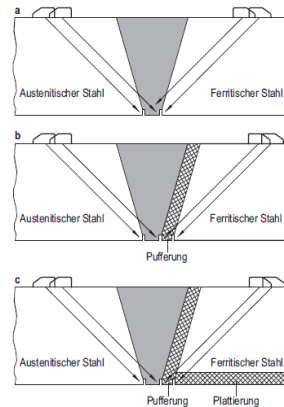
Lage der Nuten und Einschallrichtungen für die Längsfehlerprüfung von Schweißverbindungen zwischen ferritischen und austenitischen Stählen
